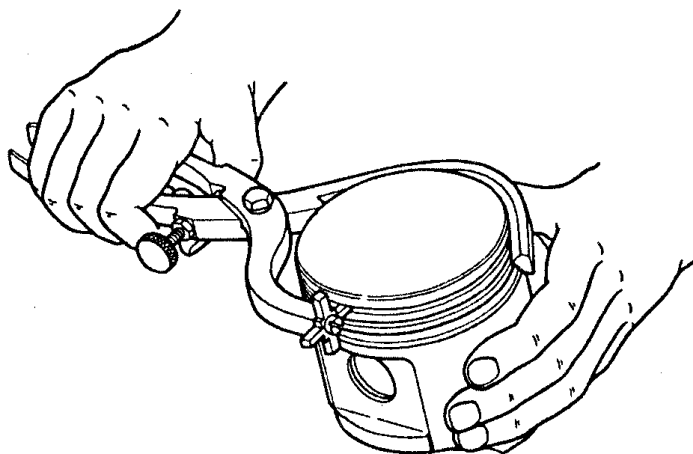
Очистка канавок поршневых колец от нагара с помощью приспособления 5-У-27691
